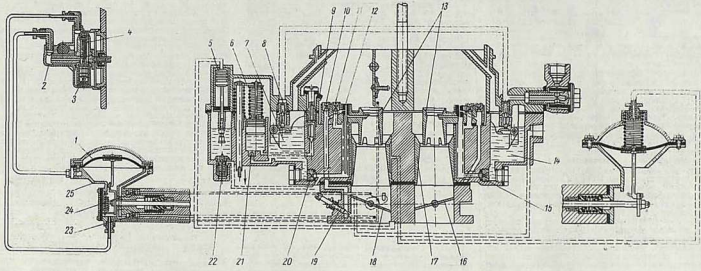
Схема четырехкамерного карбюратора K-114B с пневматическим ограничителем оборотов и вакуумным приводом вторичных заслонок: 1 — диафрагма; 2 — ротор; 3 — центральный клапан; 4 — регулировочный винт; 5 — пневматический привод экономайзера; 6 — механизм привода ускорительного насоса; 7 — поплавок; 8 — топливный клапан; 9 — распылитель ускорительного насоса; 10 — воздушный жиклер холостого хода; 11 — воздушный жиклер главной системы; 12 — топливный жиклер хо-
